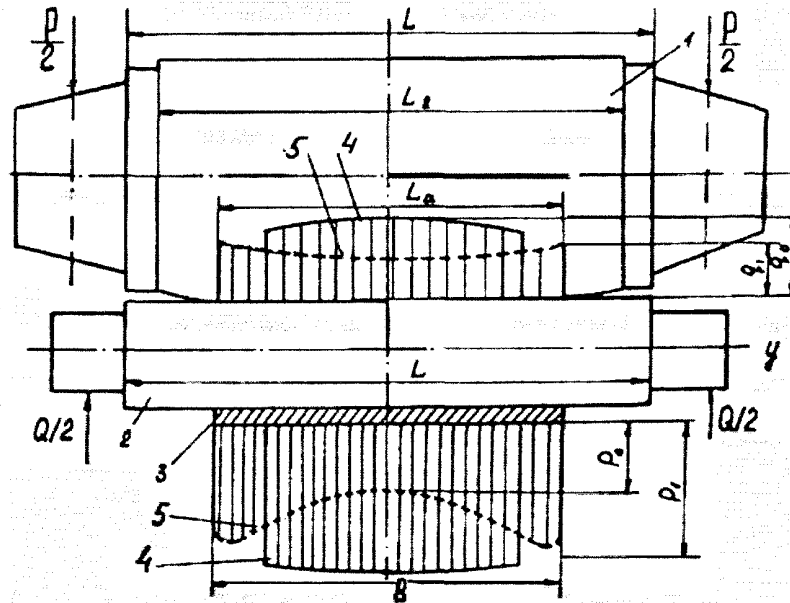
Валки до розрахунку чотирьохвалкового стана: 1 – опорний валок; 2 – робочий валок; 3 – штаба; 4 – епюри при прокатці вузьких штаб; 5 – теж при прокатці широких штаб
